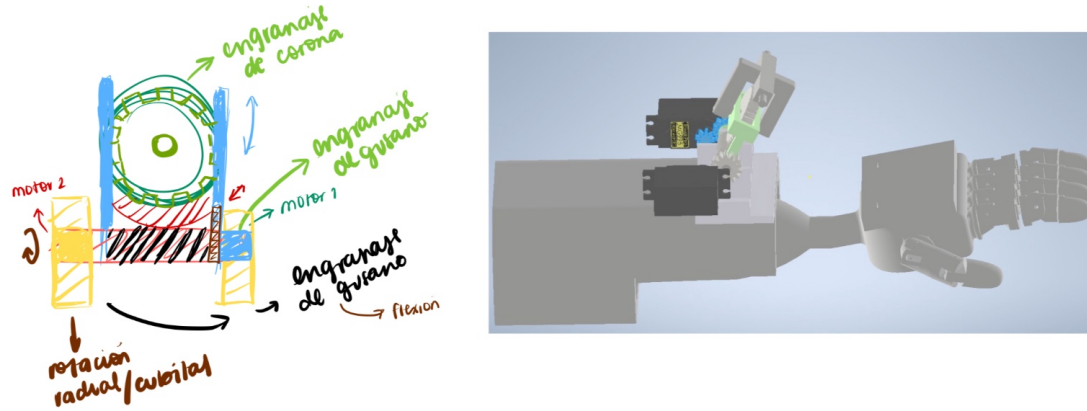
Boceto de transmisión de potencia (engranajes) con primer diseño 3D
